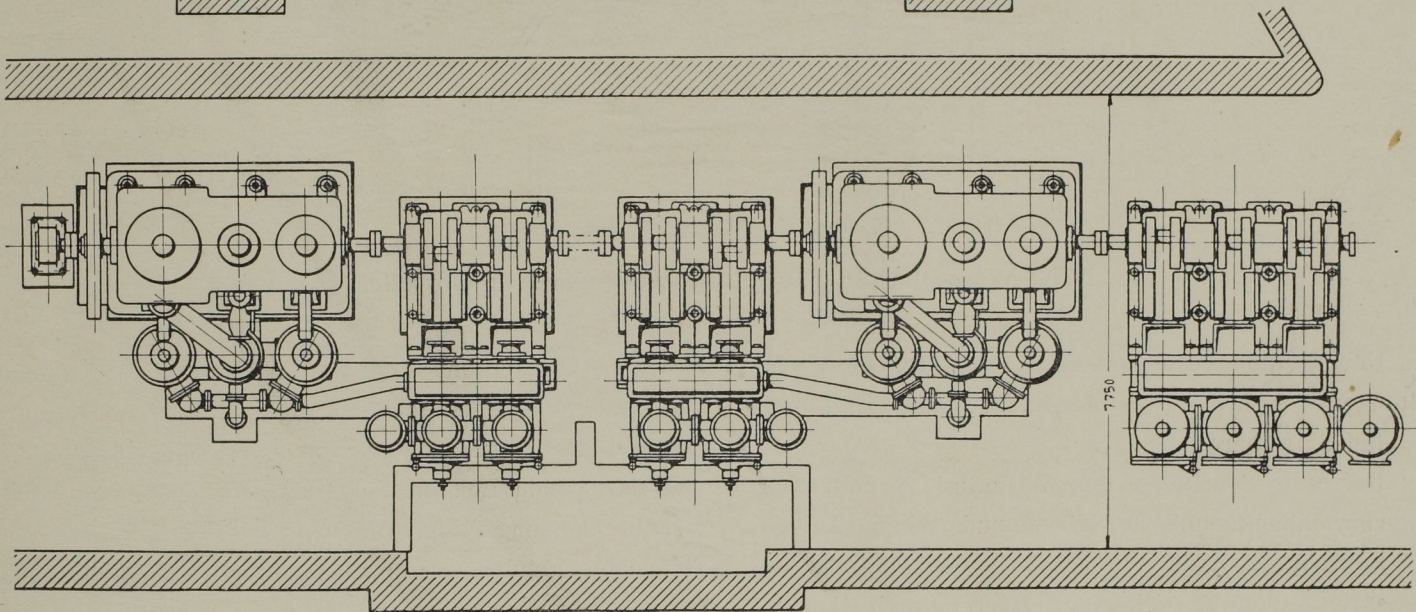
Grundriss der Anlage. Massst. 1 : 120.
